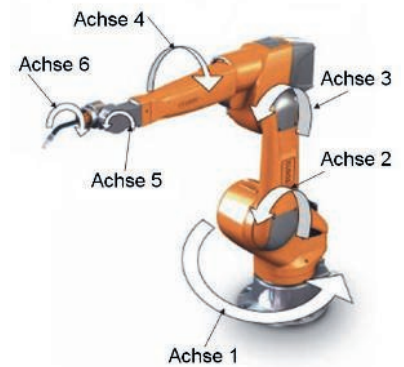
Industrieroboter zum Schweißen mit sechs Drehachsen zur optimalen Positionierung des Schweißbrenners.
